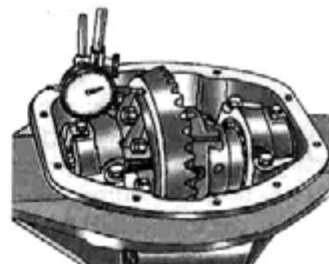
Проверка биения «затылка» ведомой шестерни
